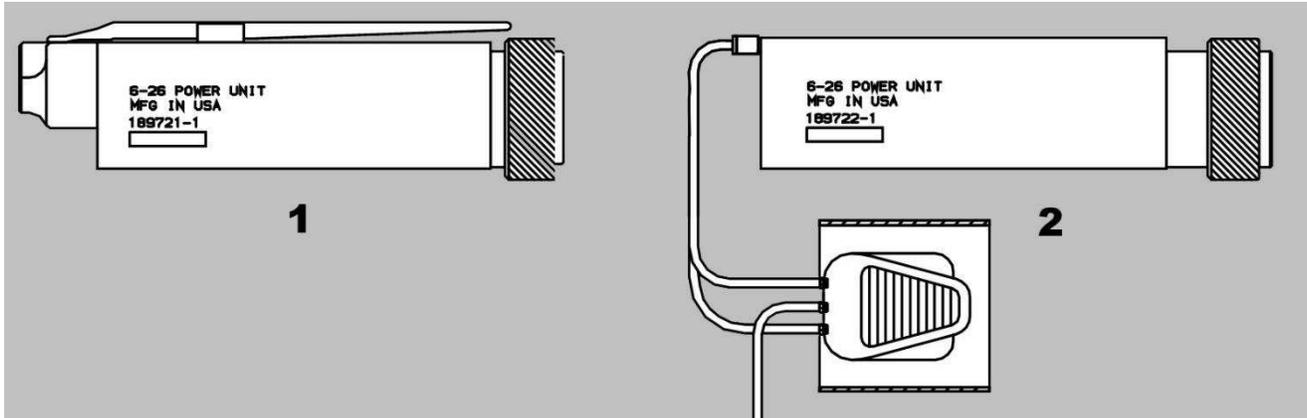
626 Pneumatikwerkzeugbaugruppen
